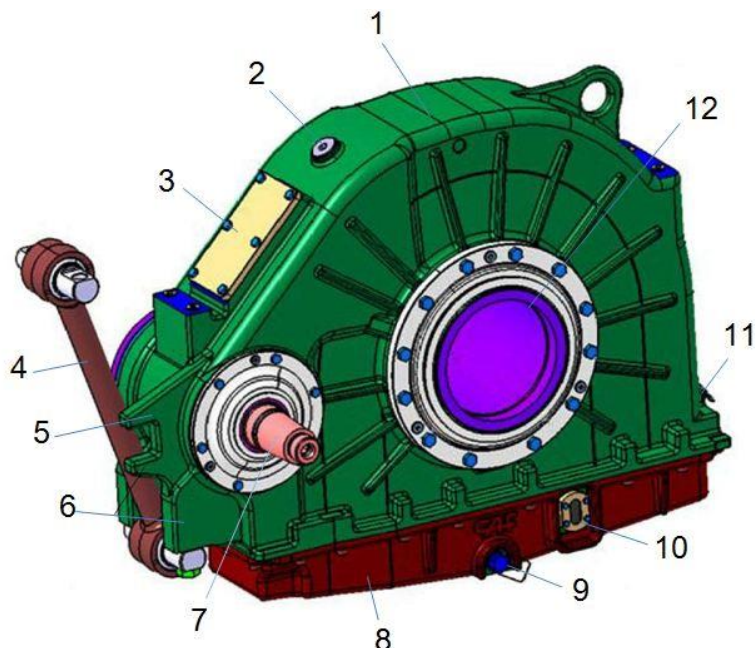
Общий вид редуктора САФ (Испания) и его составные части:
